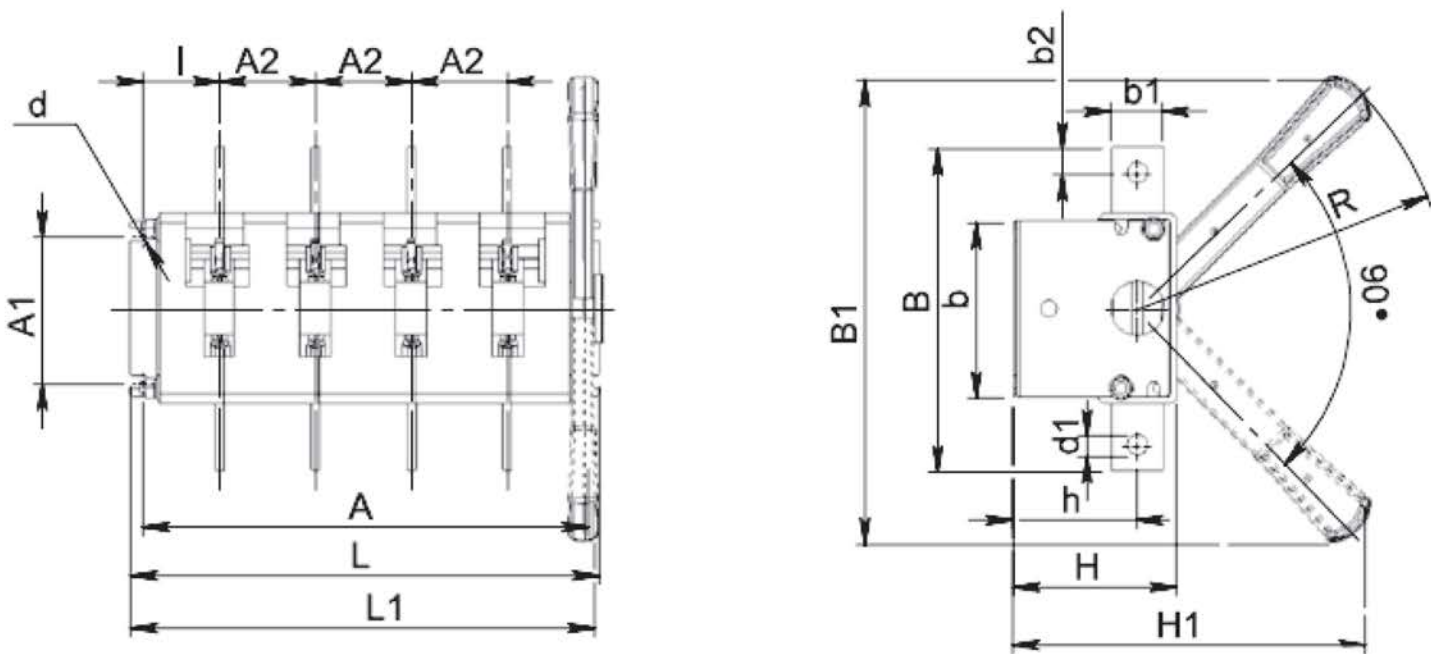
Выключатель-разъединитель четырехполюсный на одно направление с передней смещенной рукояткой.
